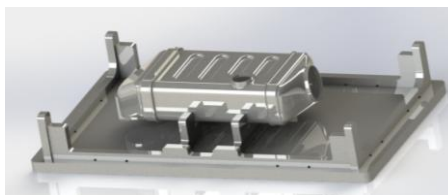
Utillaje de soldadura brazing para el horno.
